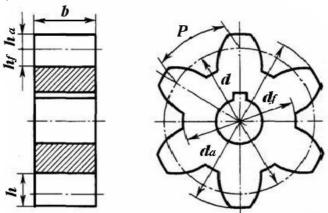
Основные элементы цилиндрического прямозубого зубчатого колеса
